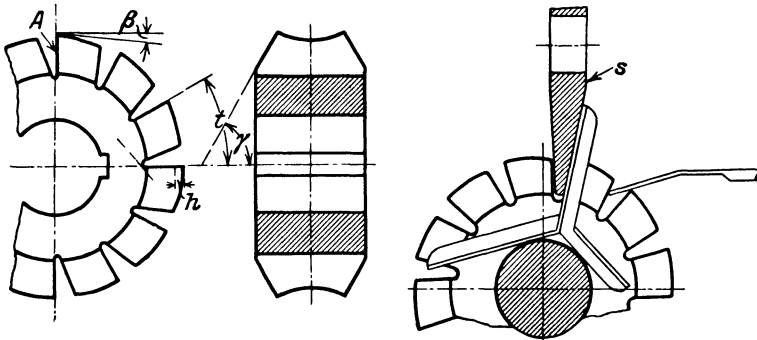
u. 24. Schleifen hinterdrehter Fräser.
